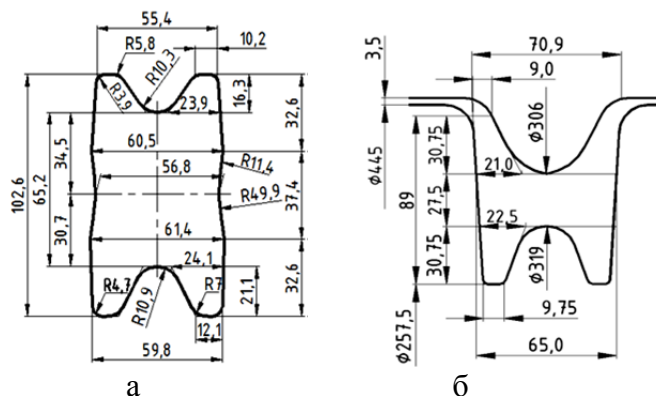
Исходная заготовка (а) и черновой закрытый балочный калибр (б)
